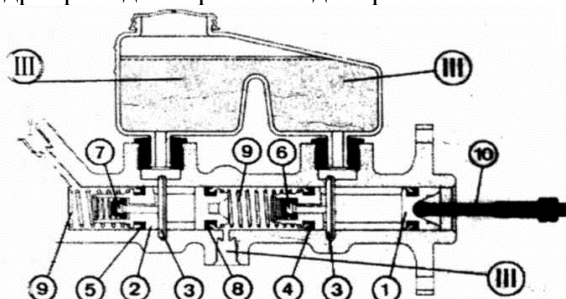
Исходное положение деталей главного цилиндра с центральными поршневыми клапанами:
